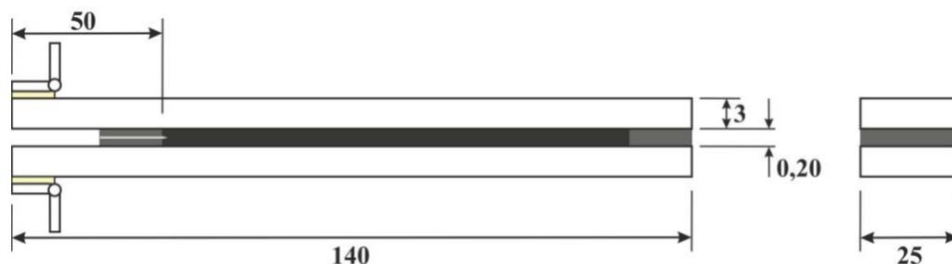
Dimensões dos provetes DCB (em mm) (adaptado de [42])
